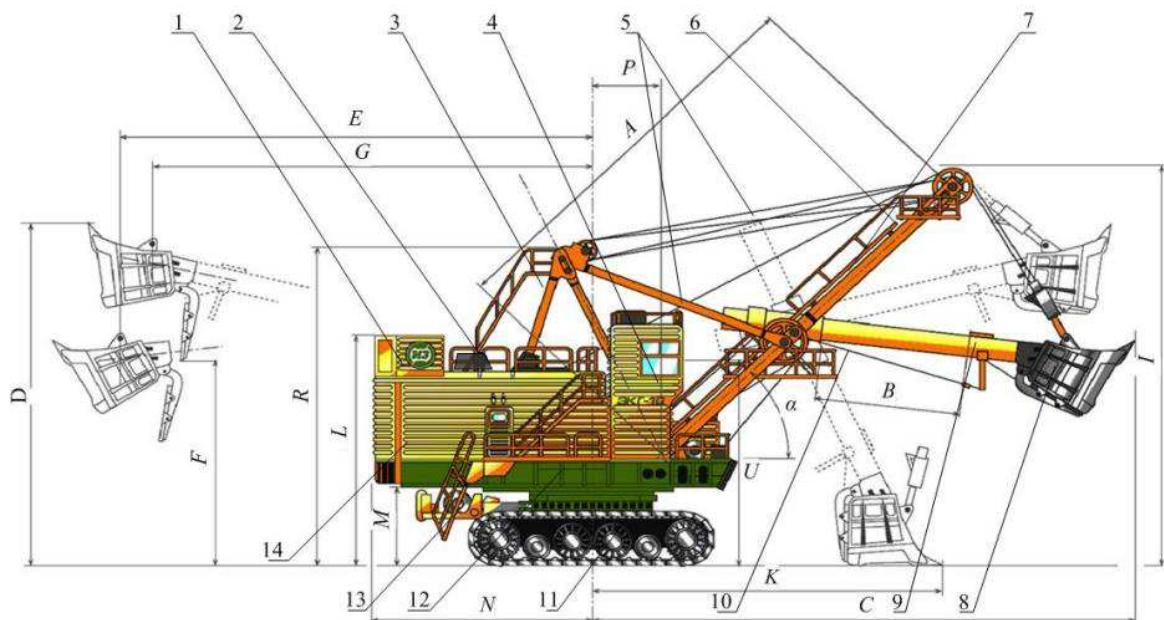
Общий вид экскаватора и схема рабочих размеров
